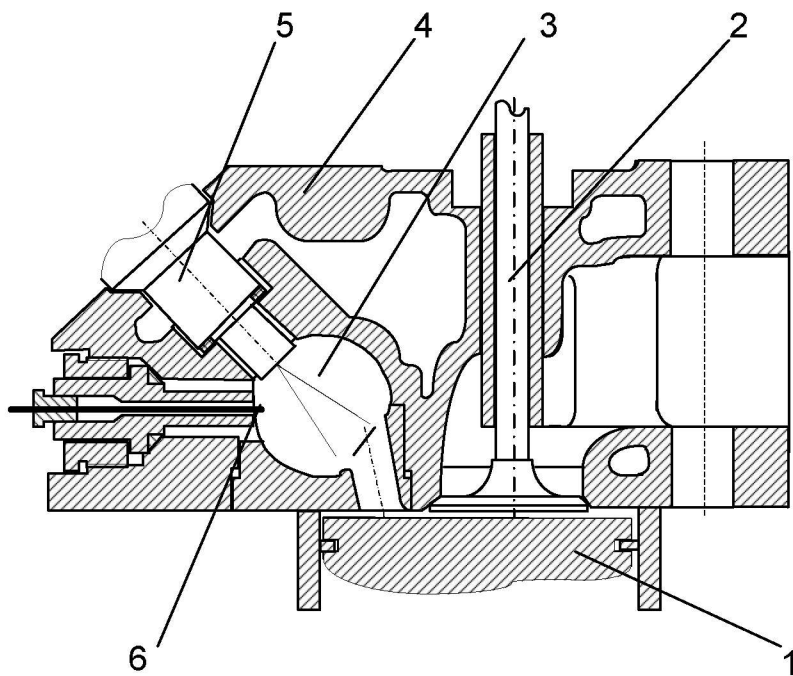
Схема камеры сгорания дизеля Ч 8,5/11: 1-поршень; 2-клапан; 3-вихревая камера сгорания; 4-головка; 5-форсунка; 6-термопара
